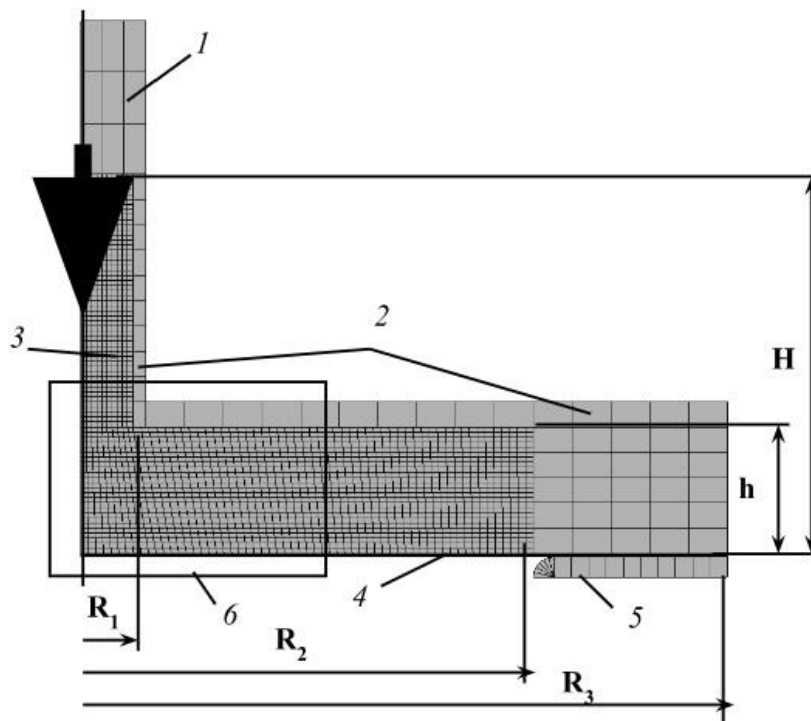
Схема розрахункової моделі (1 – жорсткий поршень, що імітує межу парогазової порожнини з високим тиском; 2 – камера; 3 – рідина; 4 – заготовка; 5 – витягувальне кільце):
